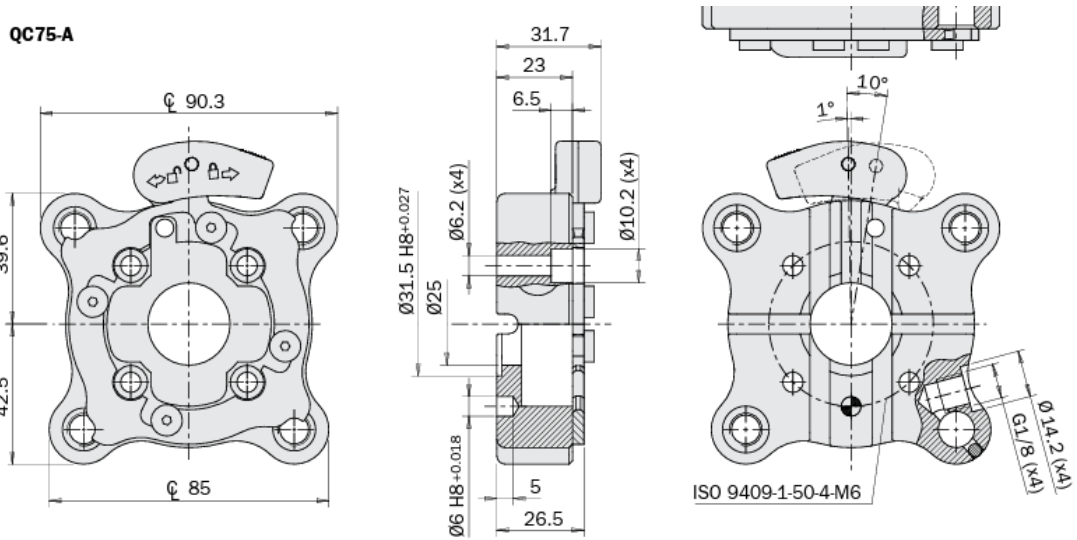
Dimensões do acoplador ligado ao robô [36].
